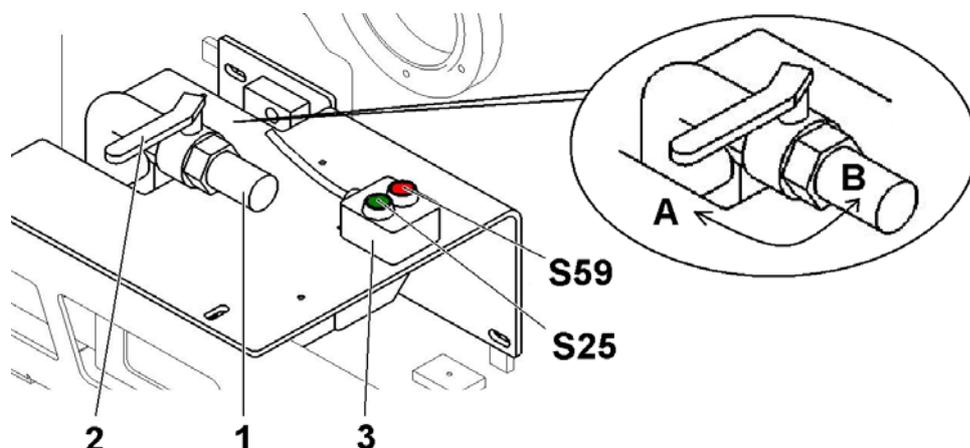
Bomba de rellenado de combustible eléctrica
